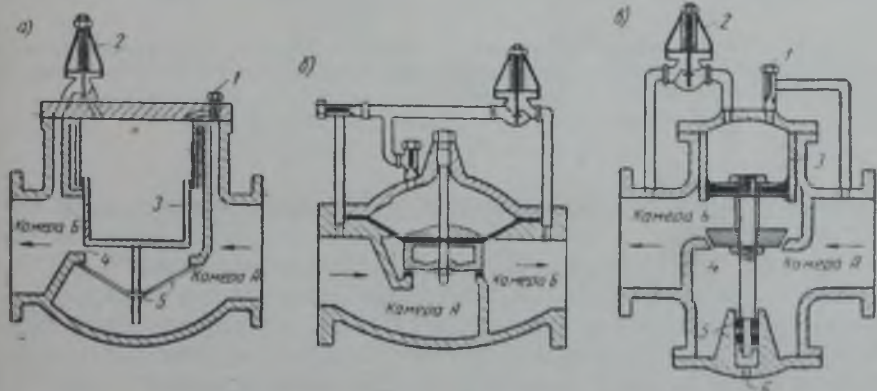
Клапаны для регулирования давления (из Water Works Eng. September, 1943, p. 827)
